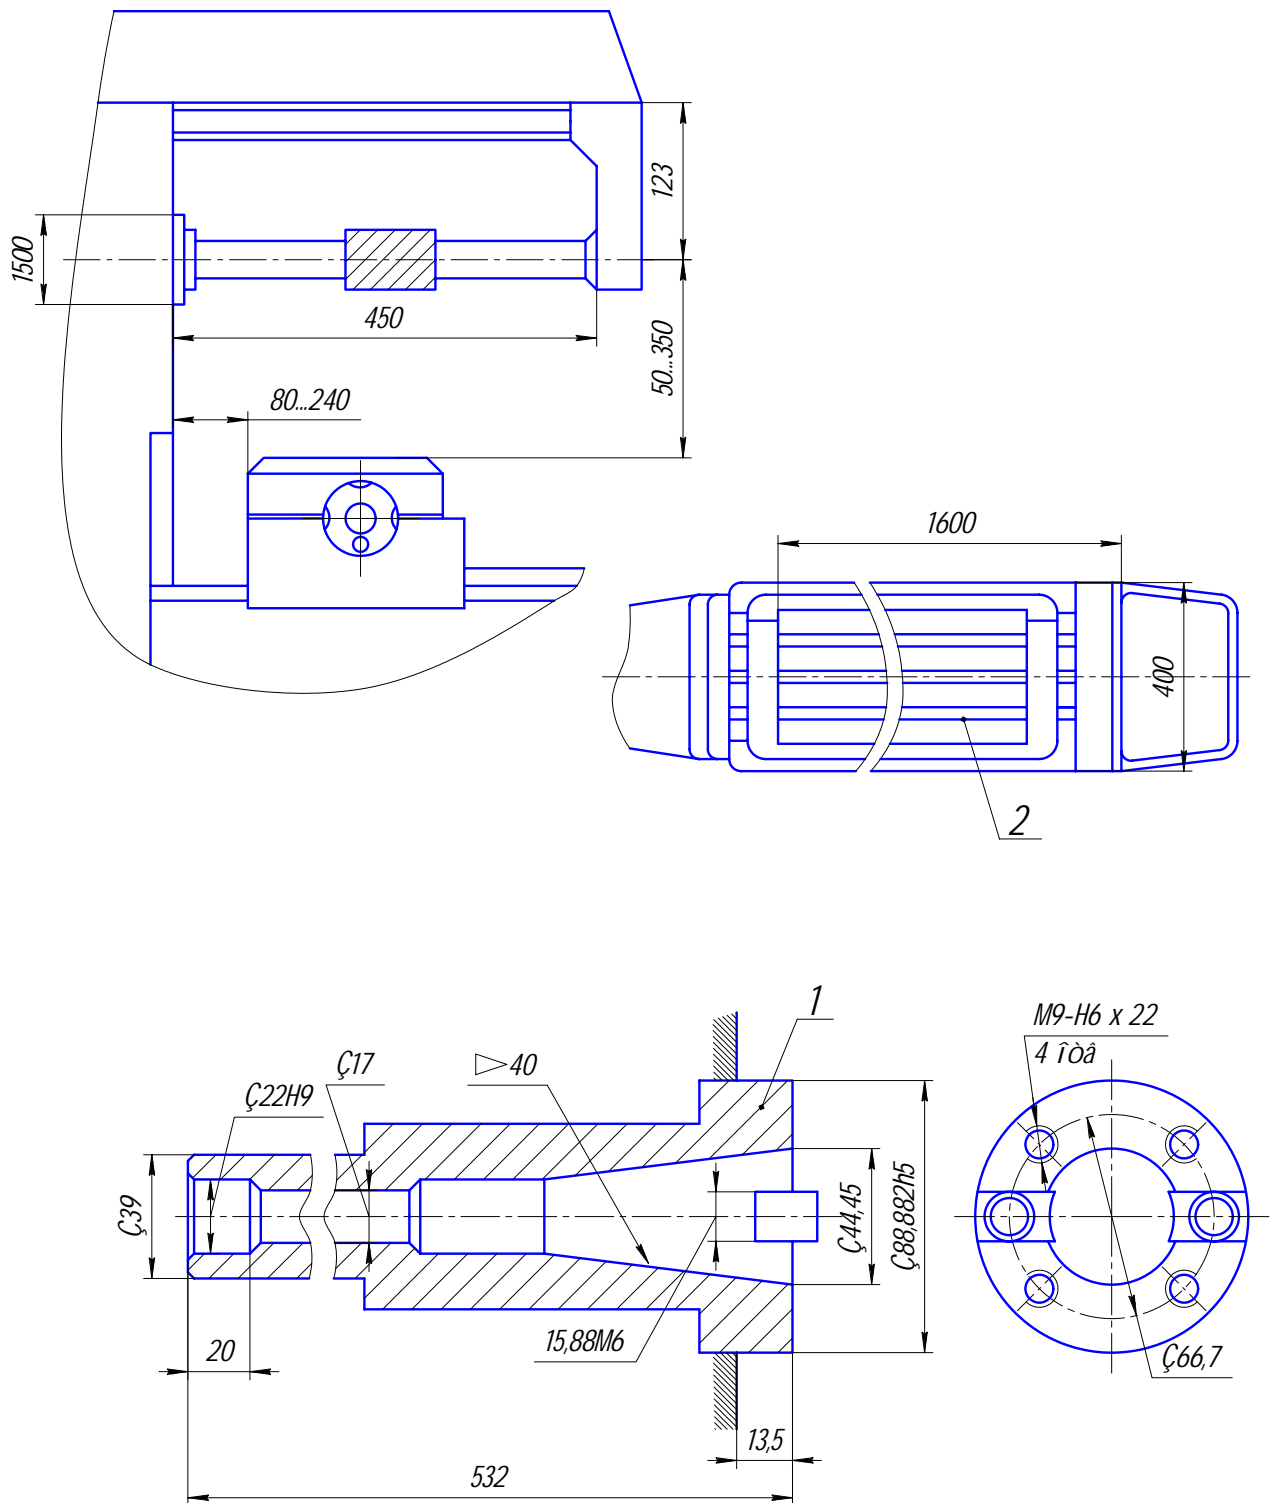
Габарити робочої зони і установочні бази горизонтально-фрезерного верстата моделі ГФ2171Р4:
